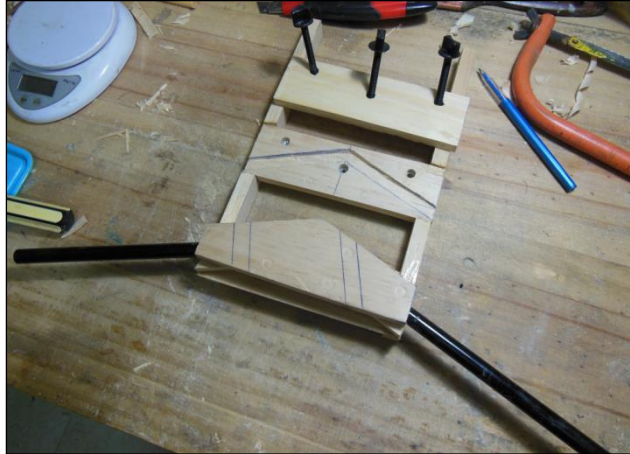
Estructura construida del primer prototipo de avión. Fuente: Autor
